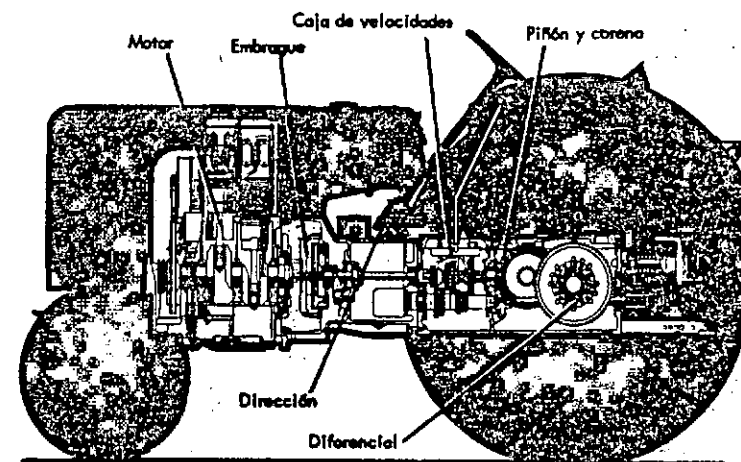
MECANISMOS PRINCIPALES DE LA TRANSMISION DE UN MOTOR
